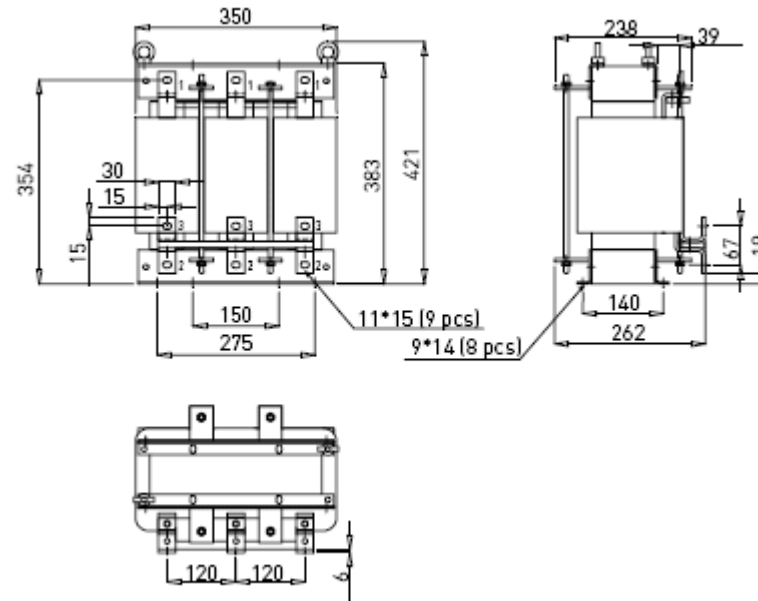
Габариты дросселя для типоразмера FR11(вес = 115 кг)
